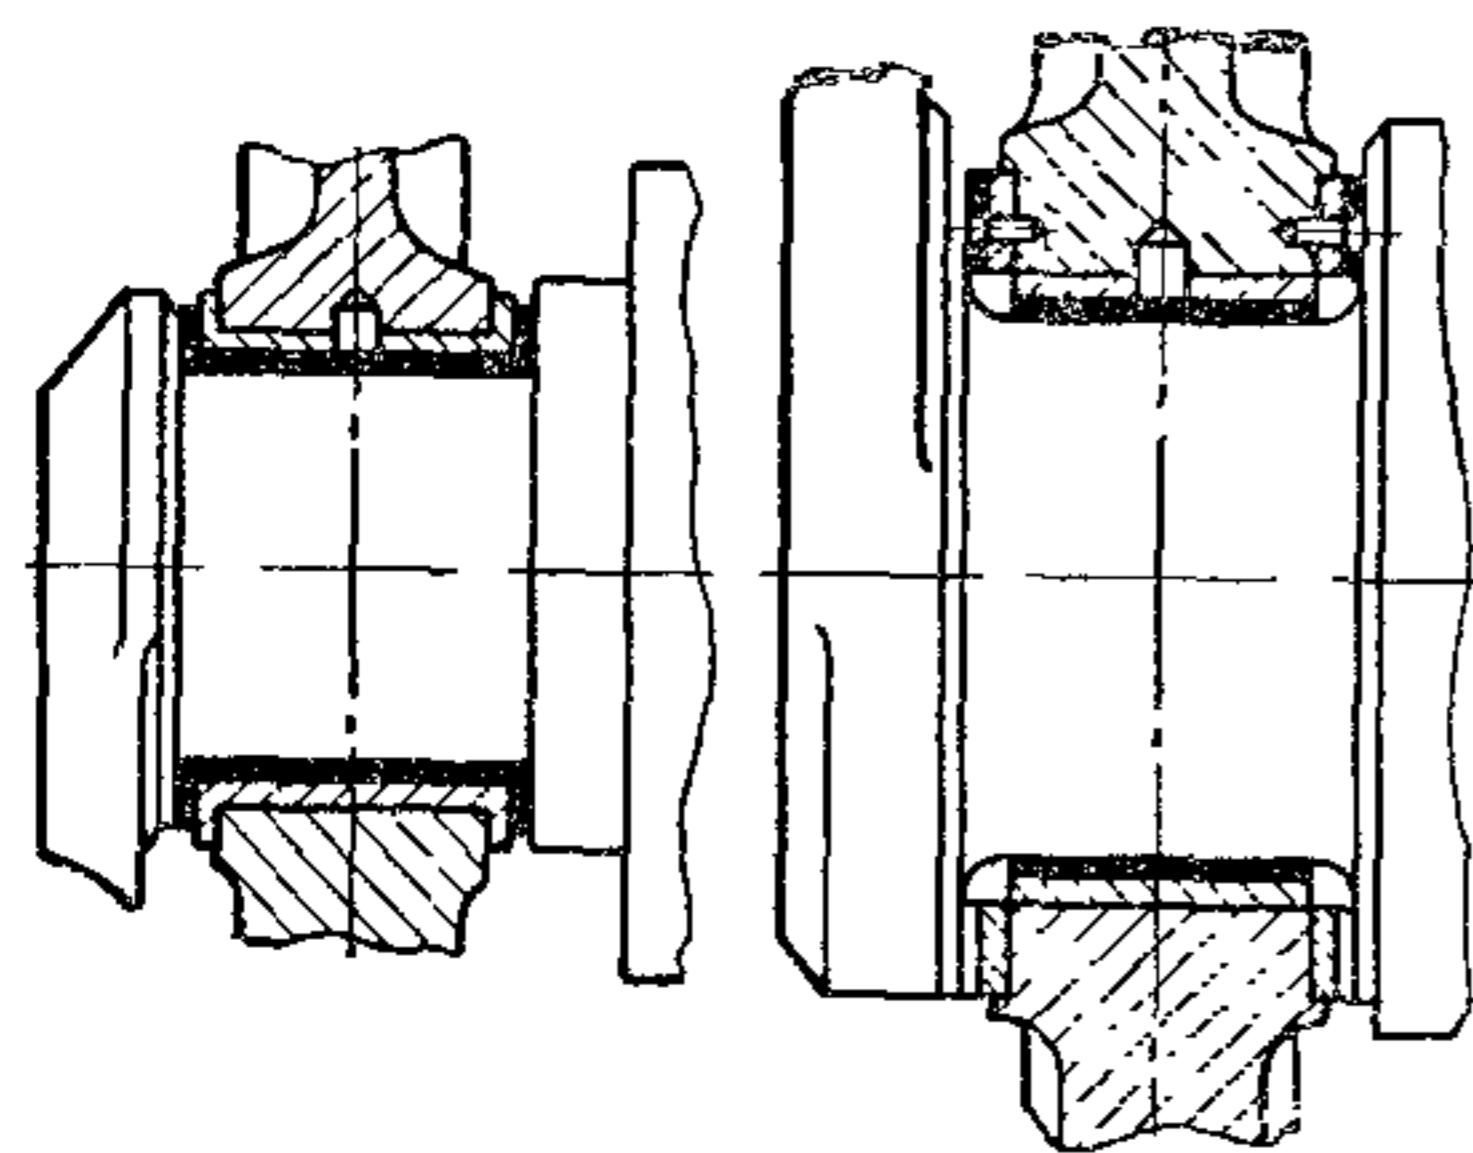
Конструкция упорно-опорных подшипников коленчатого вала
